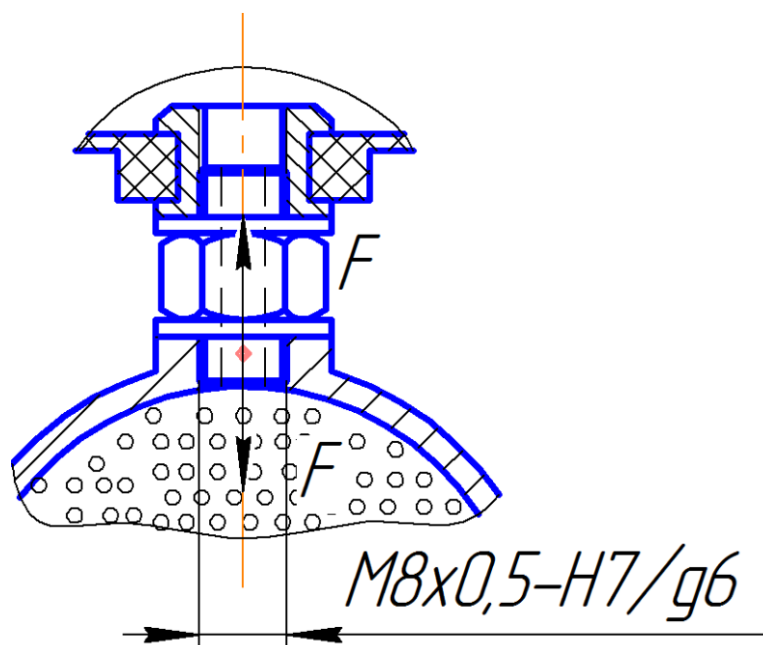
Расчётная схема резьбового соединения корпуса газогенератора и отводящего штуцера
